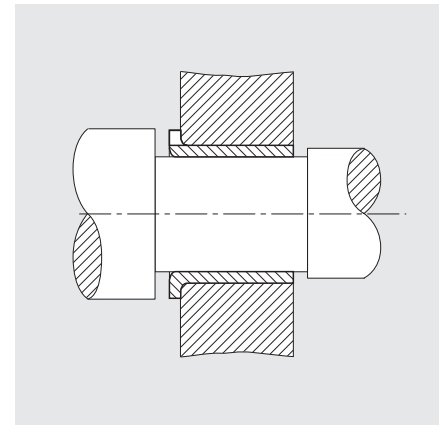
Glatte Gehäusebohrung. Axiale Fixierung geschieht durch eingesteckte Welle mit einseitig großem Bund. Aufnahme von axialen Kräften möglich.
